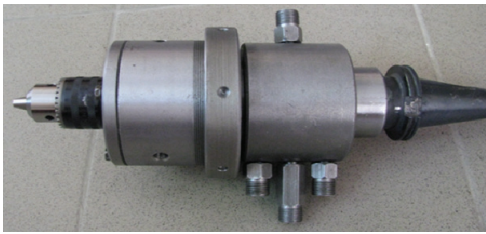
Измерительный преобразователь вращающего момента закрытого типа, предназначенный для установки в шпиндель станка
